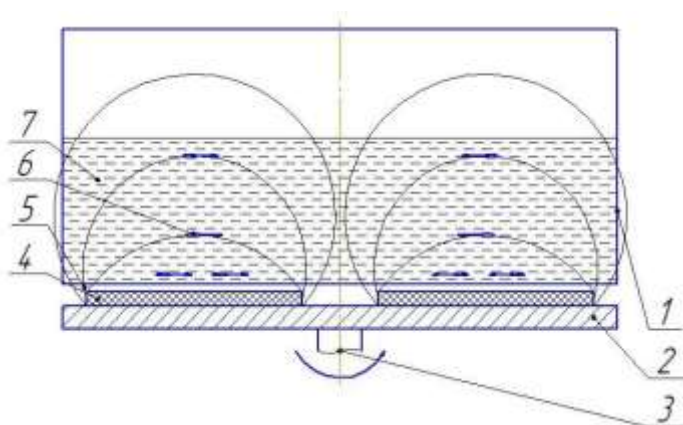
Схема магнитного галтования: 1 – Рабочий объем; 2 – подвижный диск; 3 – передающий вал; 4 – постоянный магнит; 5 – магнитное поле; 6 – галтовочный наполнитель; 7 – смазочно-охлаждающая среда
